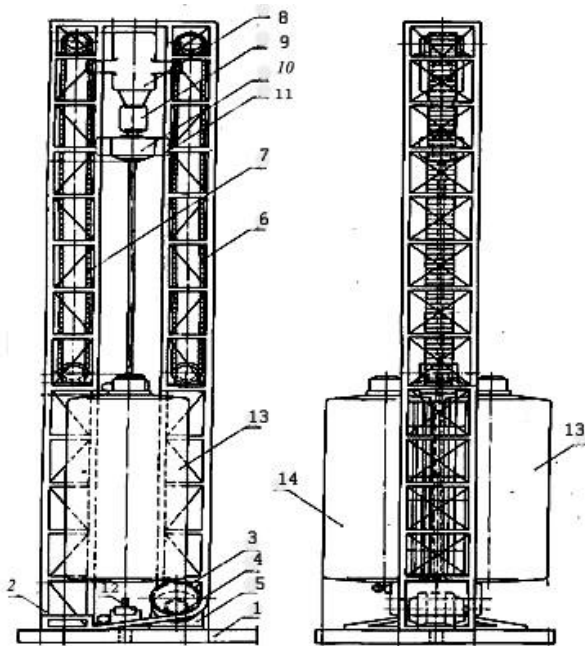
Буровой агрегат установки СБУ -300 "БУРАН"
